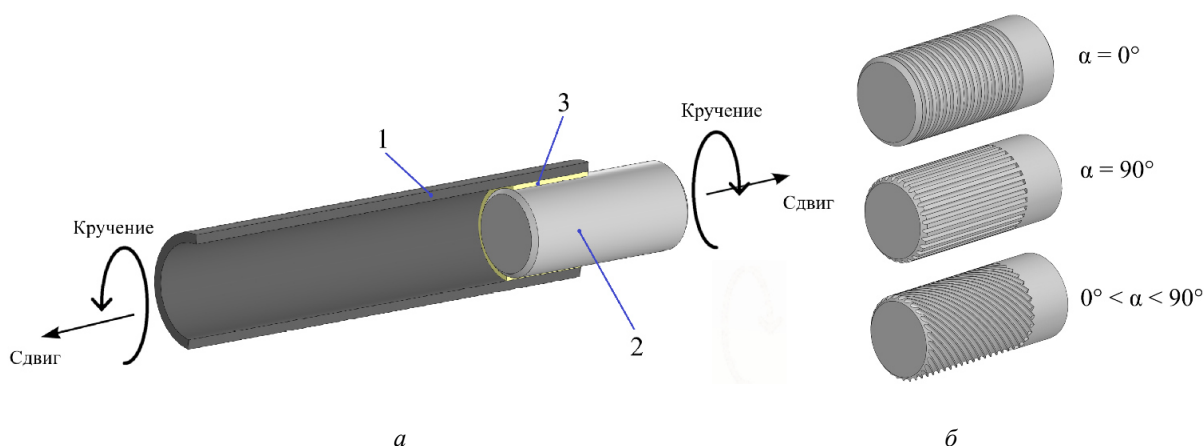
Схема клеевого соединения цилиндрических деталей:
